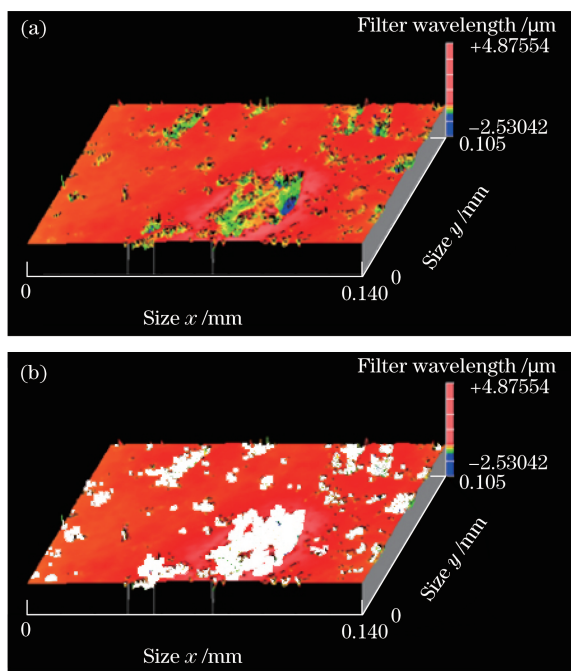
工件表面缺陷提取。(a)工件原形貌;
